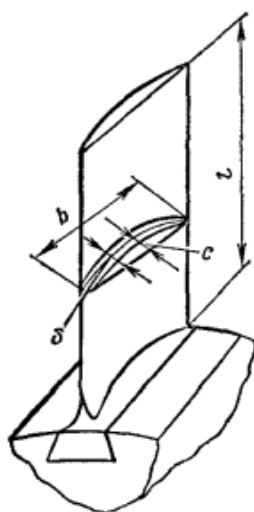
Схема рабочей лопатки осевого компрессора
